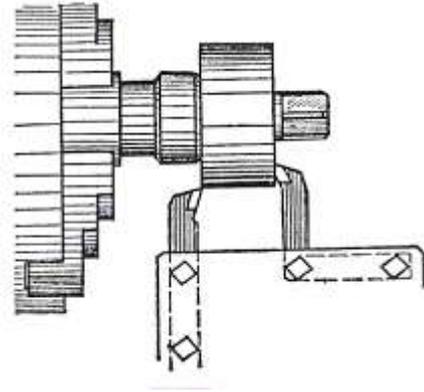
Обработка торцов втулки одновременно двумя резцами.
